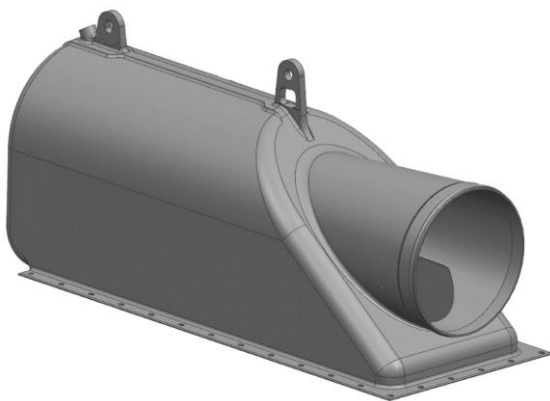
Vista Isométrica del Modelo CAD de Casting
